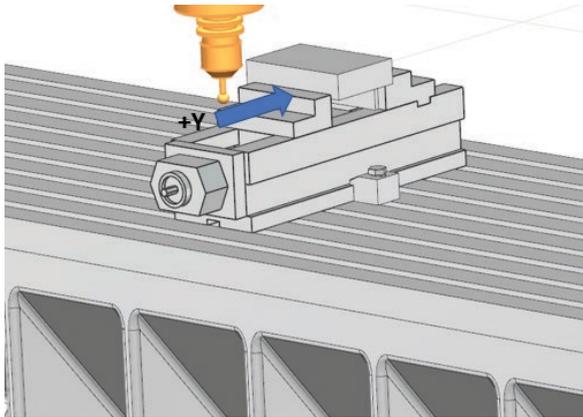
Vermessung des Werkstücks in Y-Richtung
